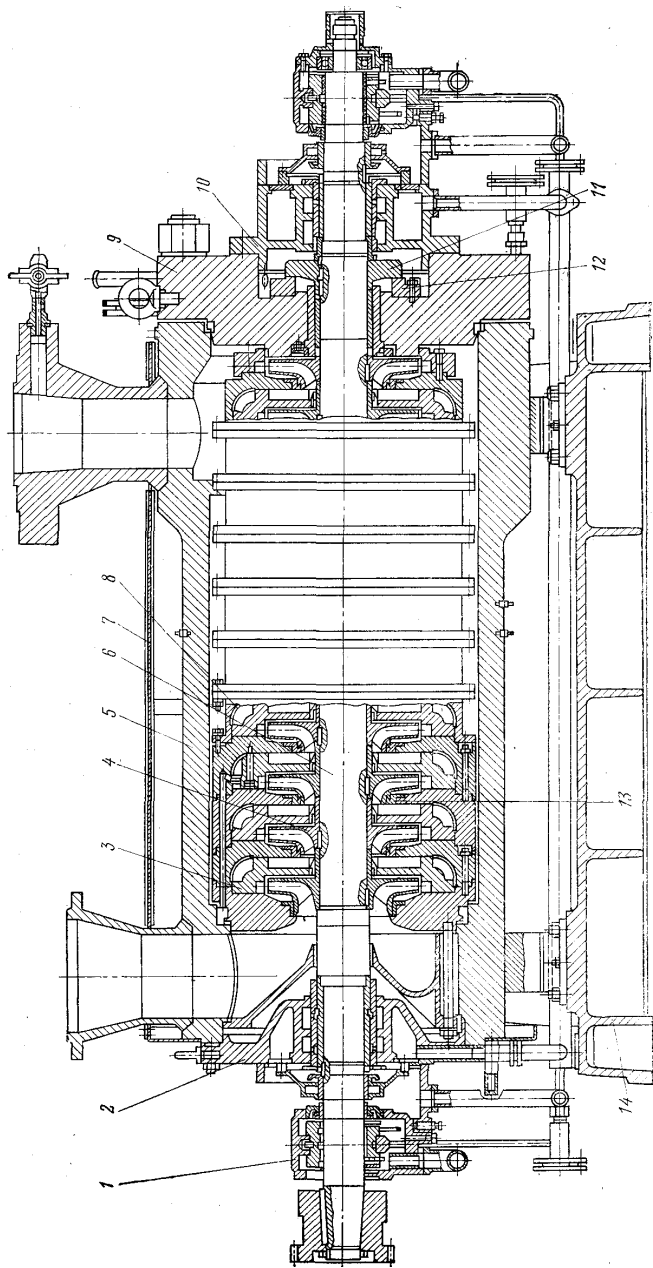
Питательный насос: 1 – подшипник скольжения; 2 - крышка входная; 3 – переднее уплотнение колеса; 4 – рабочее колесо; 5 – наружный корпус; 6 – вал; 7 – кожух; 8 – внутренний корпус; 9 – крышка напорная; 10 – корпус уплотнения; 11 – диск разгрузочный; 12 – подушка пяты; 13 – уплотнение промежуточной ступени; 14 – плита
